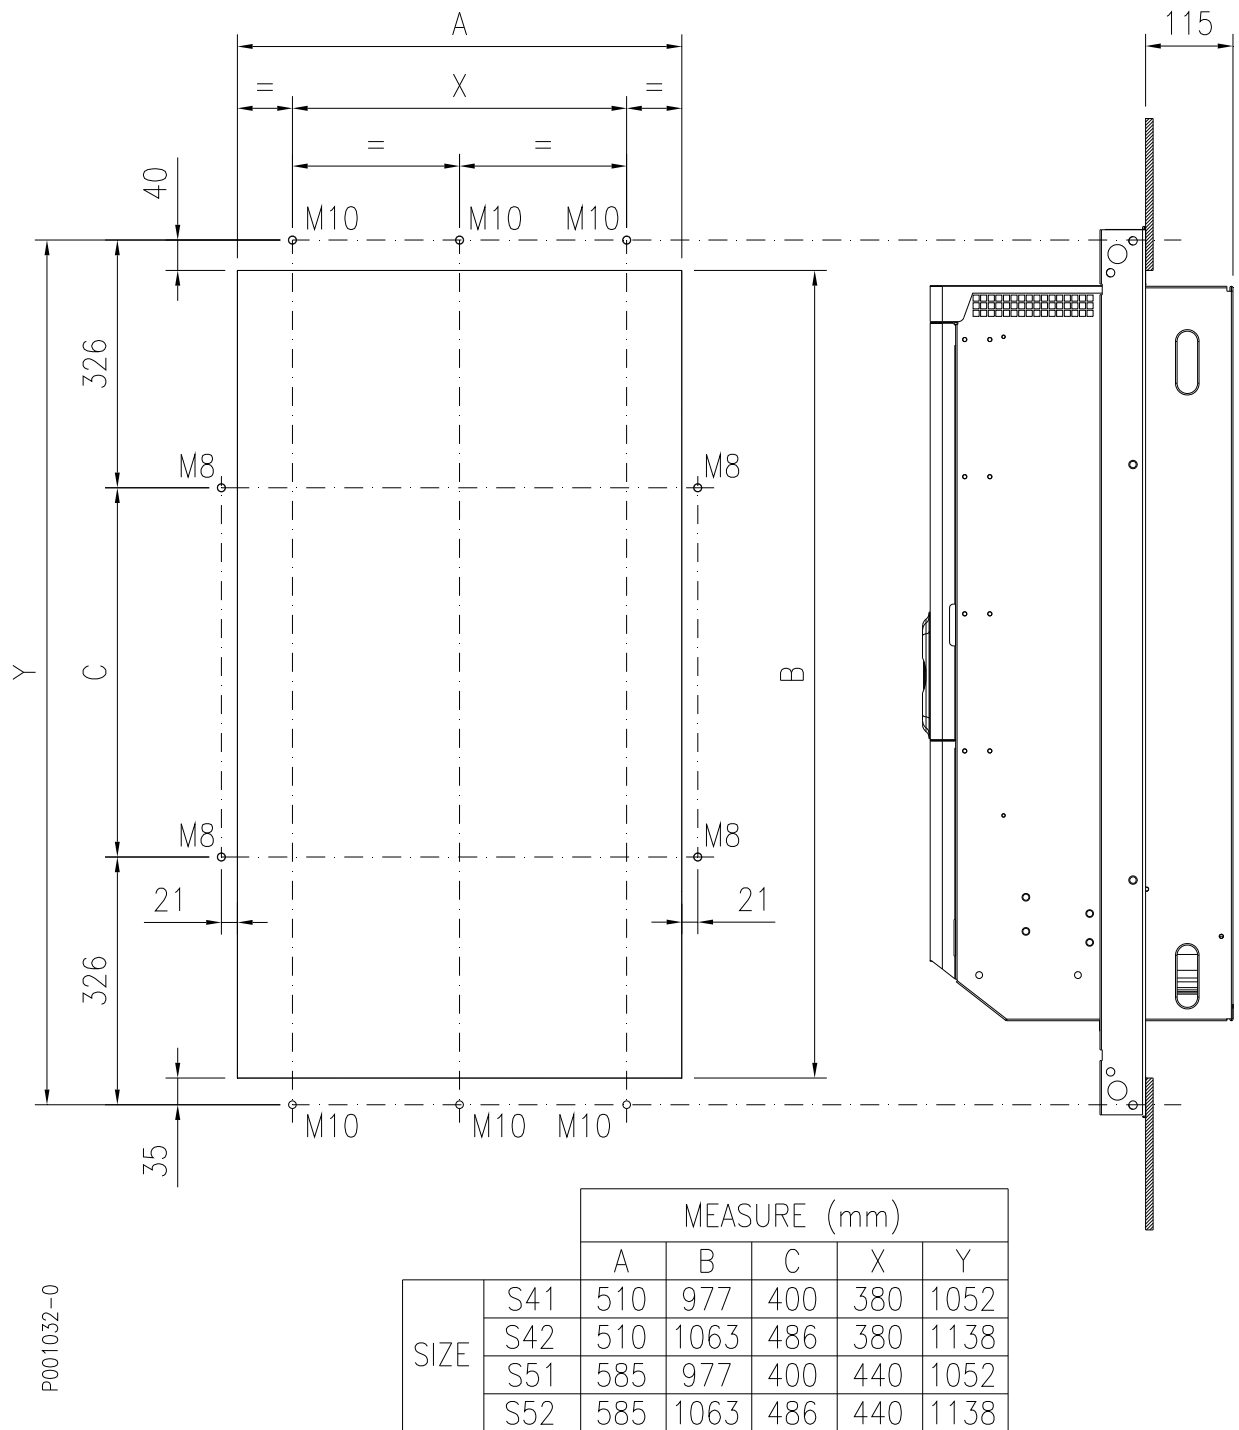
Dimensões de furação do painel para montagem passante SINUS PENTA S41, S42, S51, S52
